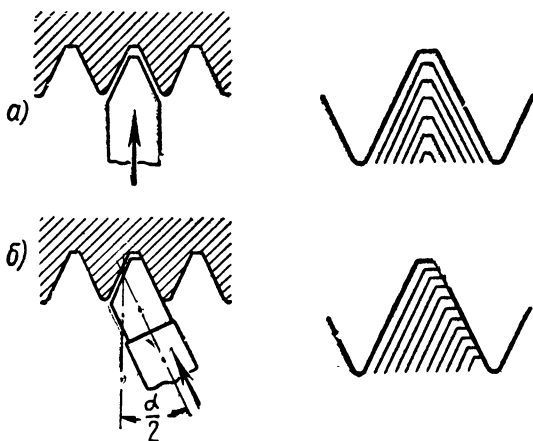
Способы установки и подачи резьбового резца при нарезании резьбы:
